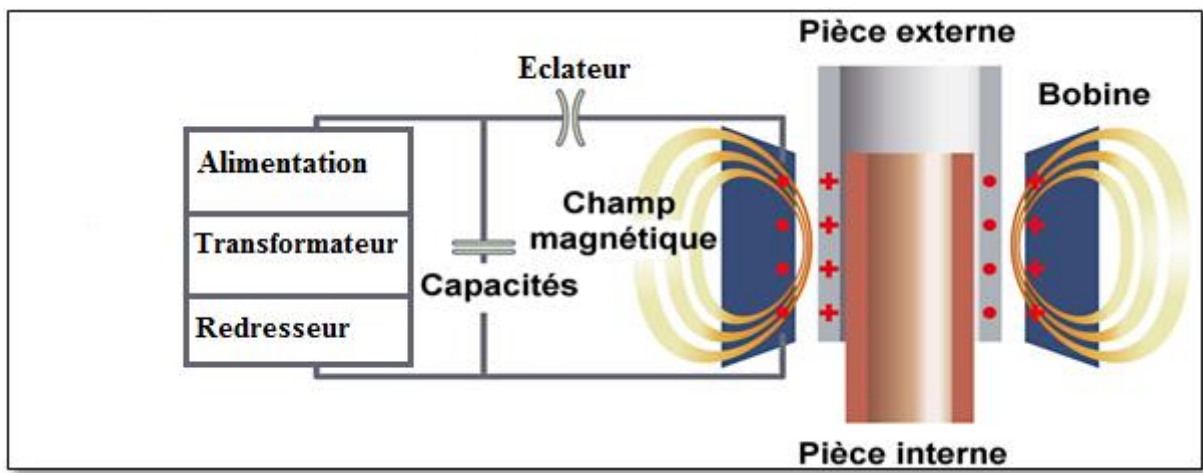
Principe de fonctionnements du soudage par impulsion magnétique [12]
